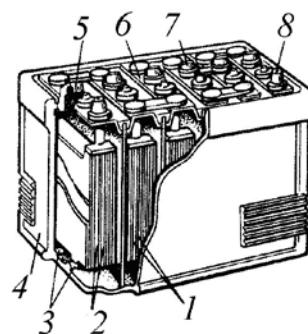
Аккумуляторная батарея: 1 – отрицательные пластины; 2 – положительные пластины; 3 – ребра; 4 – бак; 5 – пробка; 6 – крышка; 7 – соединительная перемычка; 8 – полюсной штырь; 9 – сепаратор
